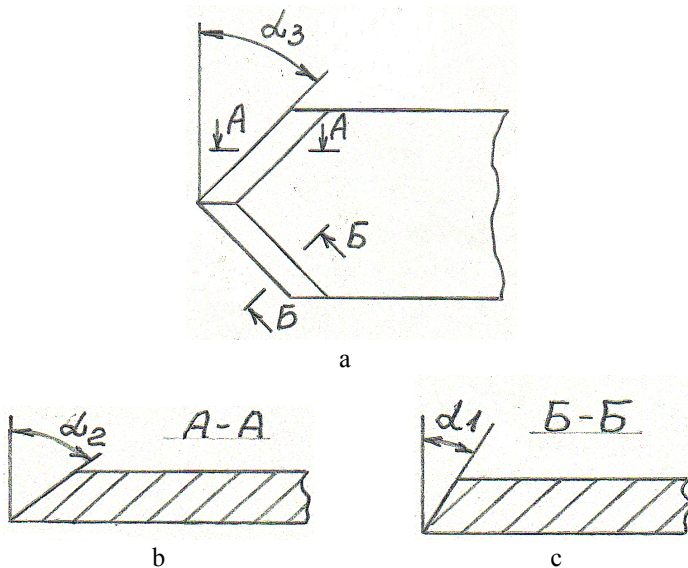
Углы наклона, заточки и резания зубьев корпуса:
